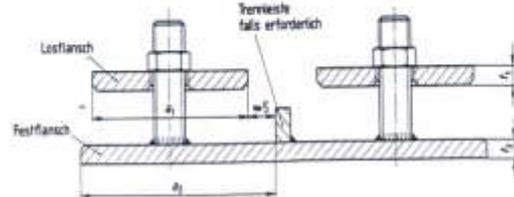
Los- und Festflanschkonstruktion in Doppelauführung für Übergänge
